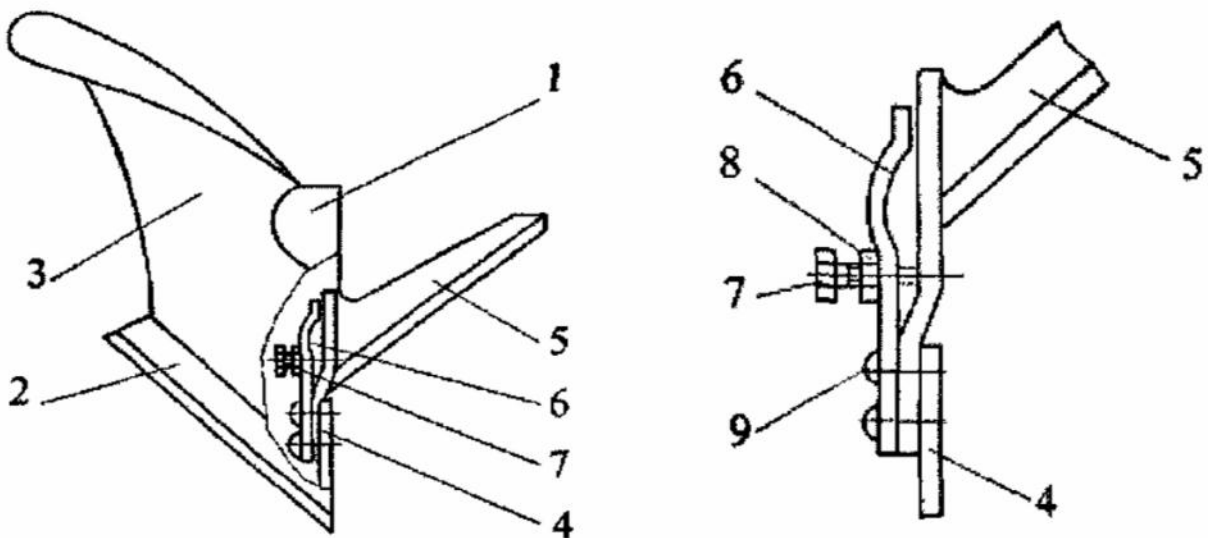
Корпус плуга з плоскорізальною лапою [107]
